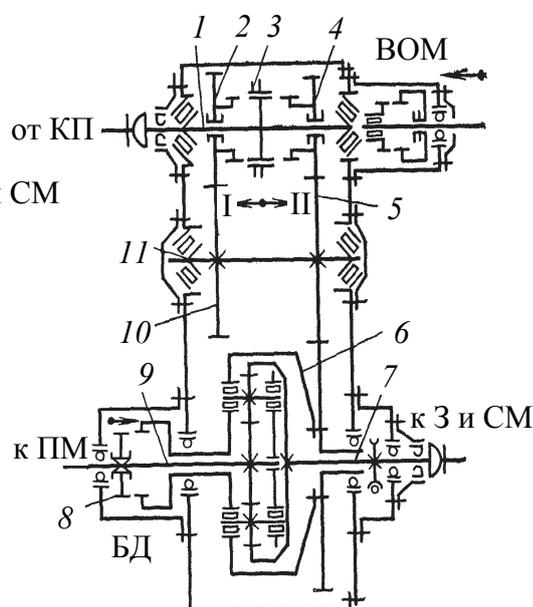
Схема раздаточной коробки с дифференциальным приводом:
